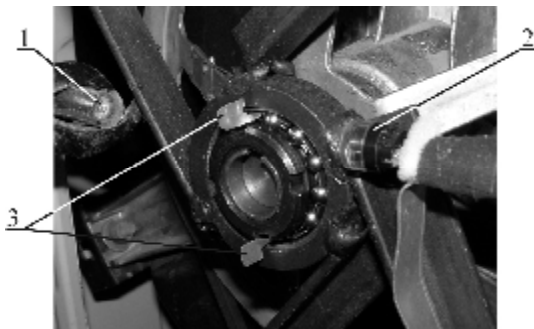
Пристрій для вимірювання числа обертів сепаратора підшипника:
